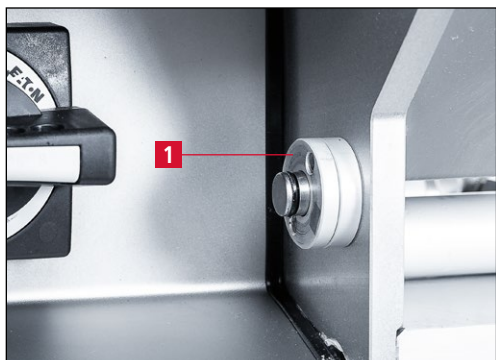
Регулировочные шайбы для настройки угла заточки
